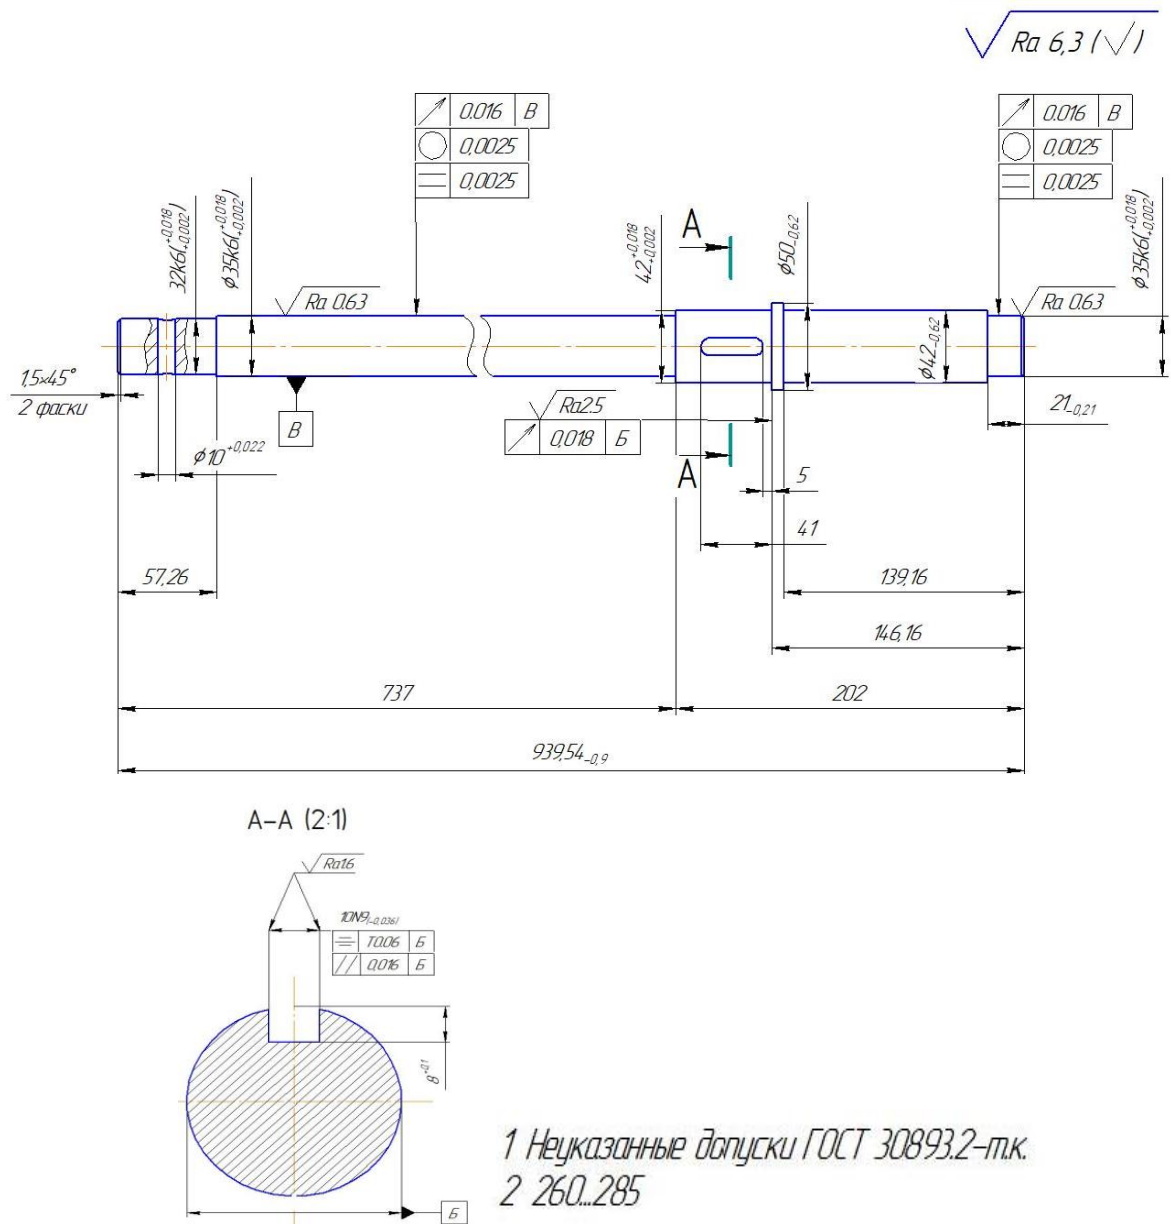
Фрагмент чертежа детали «Вал»
